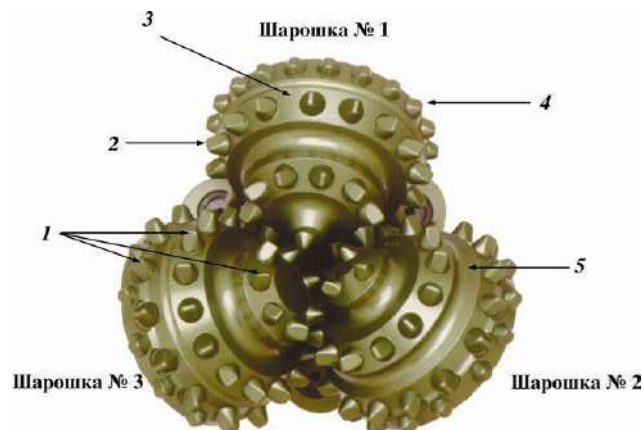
Основные элементы шарошек долота с фрезерованным вооружением: 1 – центральная точка; 2 – уменьшенный зубец; 3 – зубцы калибрующего венца; 4 – защитное покрытие; 5 – межвенцовая канавка; 6 – зазор между зубцами.
